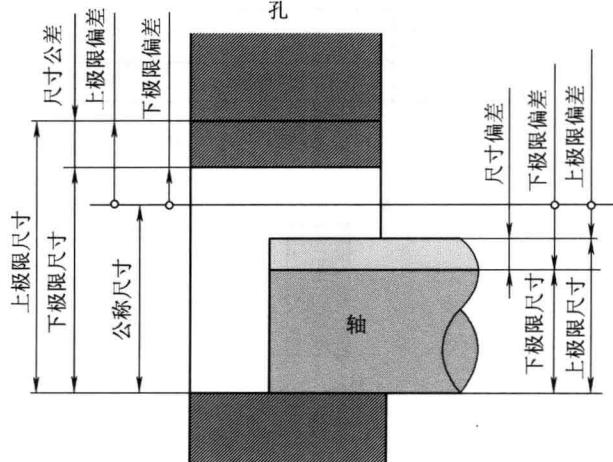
公称尺寸、极限尺寸和极限偏差、尺寸公差示意图
